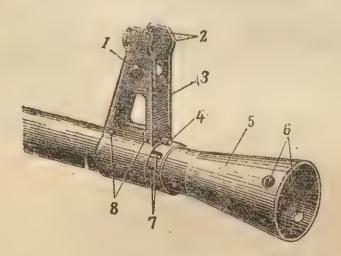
Пламегаситель и основание мушки: 1—отверстие для полозка мушки; 2— предохранитель мушки; 3— основание мушки; 4— фиксатор; 5— пламегаситель; 6— отверстия для выколотки (звена шомпола); 7— выемки для фиксатора; 8— штифты
